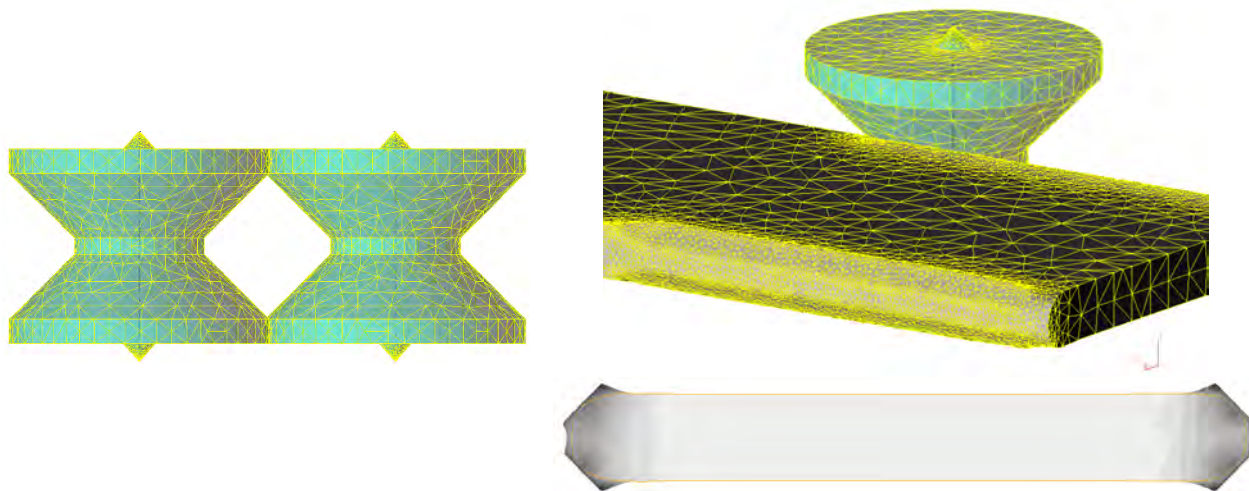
Общий вид эджерных валков, сетка на кромках и форма краевых кромок заготовки
